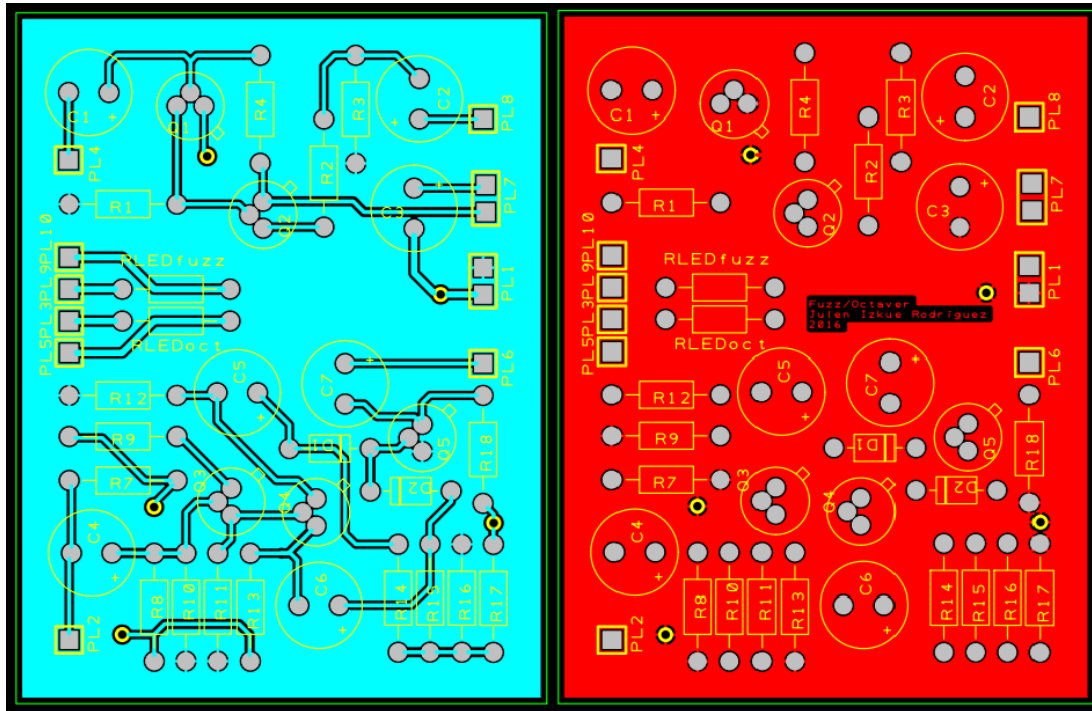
VISTAS DE LOS DOS PLANOS DEL PCB DISEÑADO
